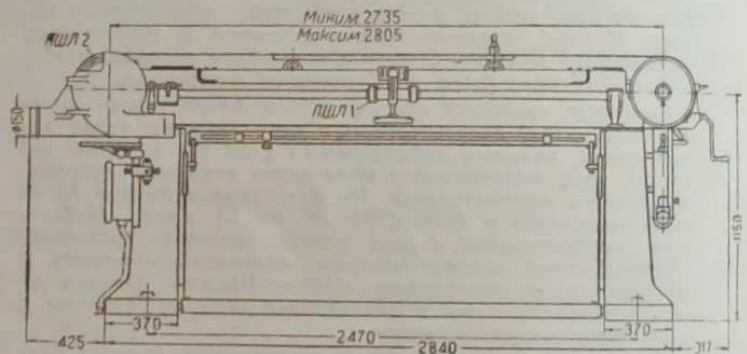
Шлифовально-ленточный станок с подвижным столом
